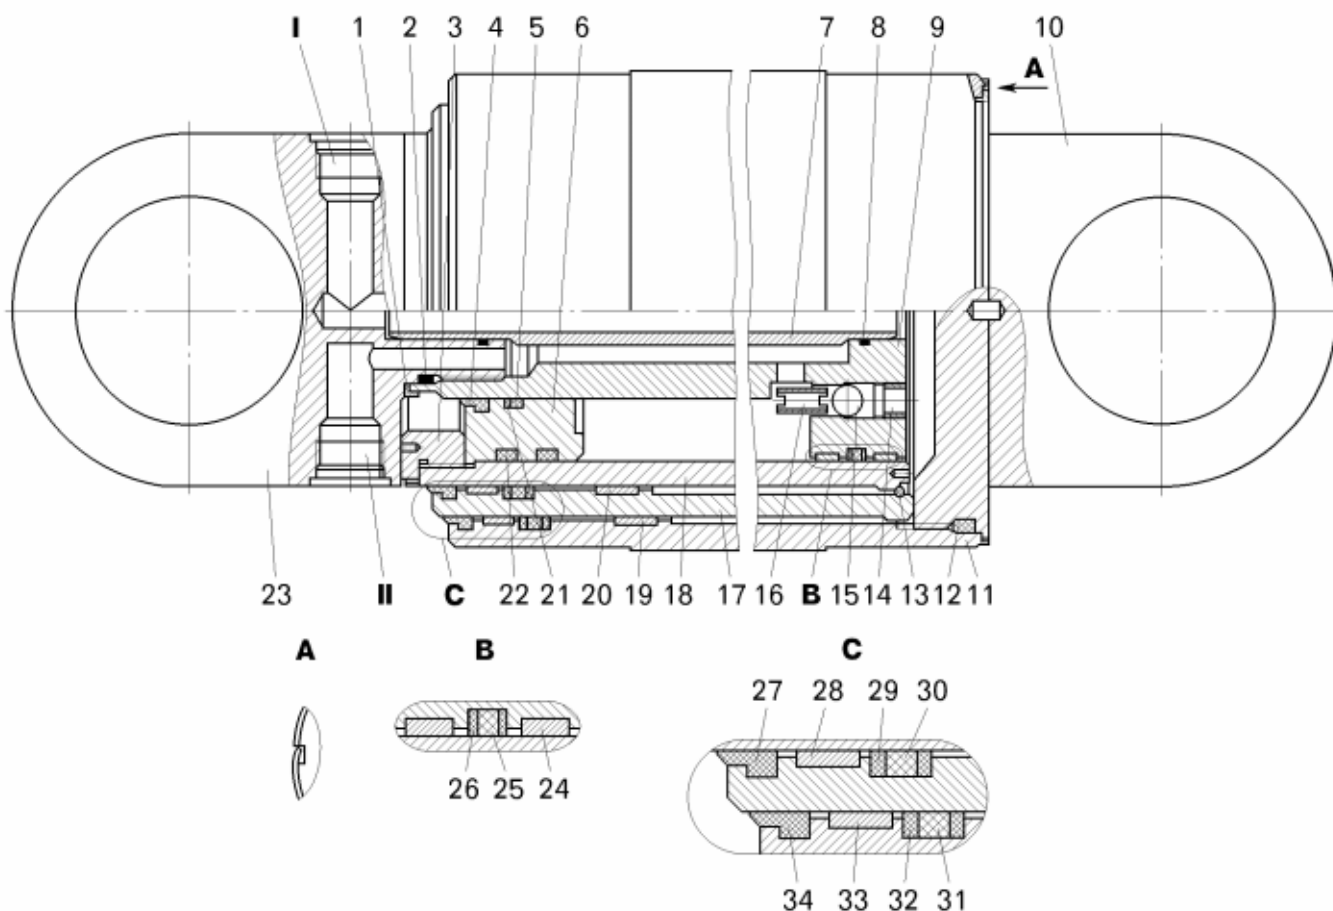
Цилиндр опрокидывающего механизма:
